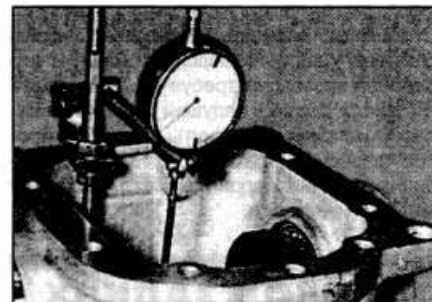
Установка индикатора на приспособление, имитирующее дифференциал
